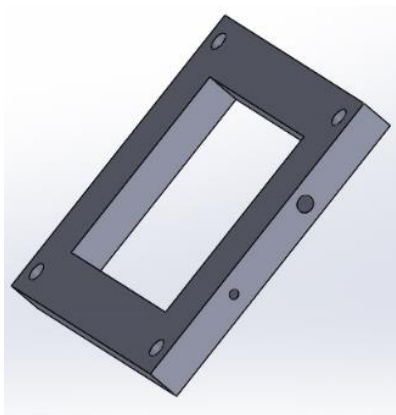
Molde diseñado para la deposición del PDMS. Realizado en SolidWorks por el GM-US.
